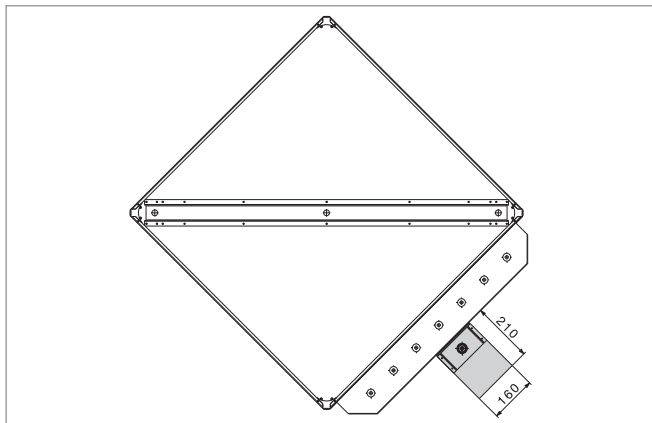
Maßbild Adapter für Ausführung F (in mm)
